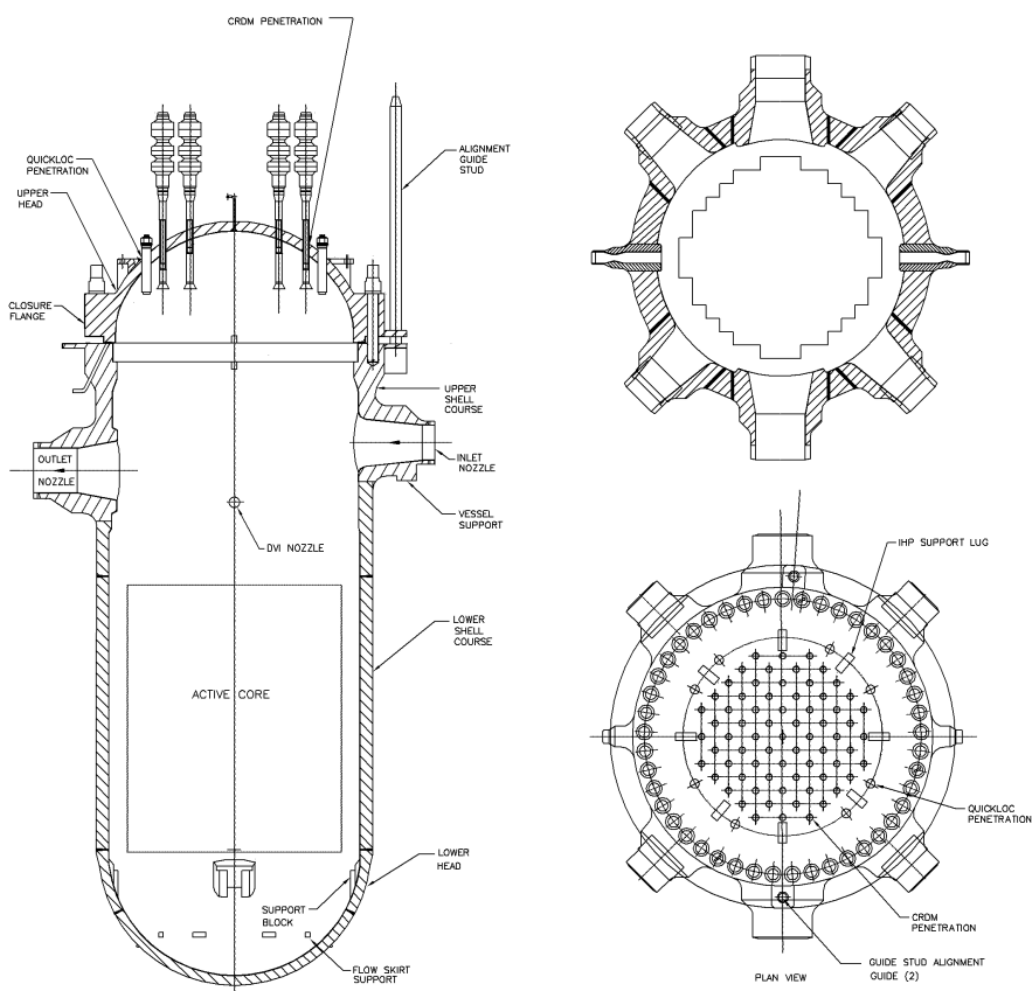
Конструкція корпусу реактора AP1000
